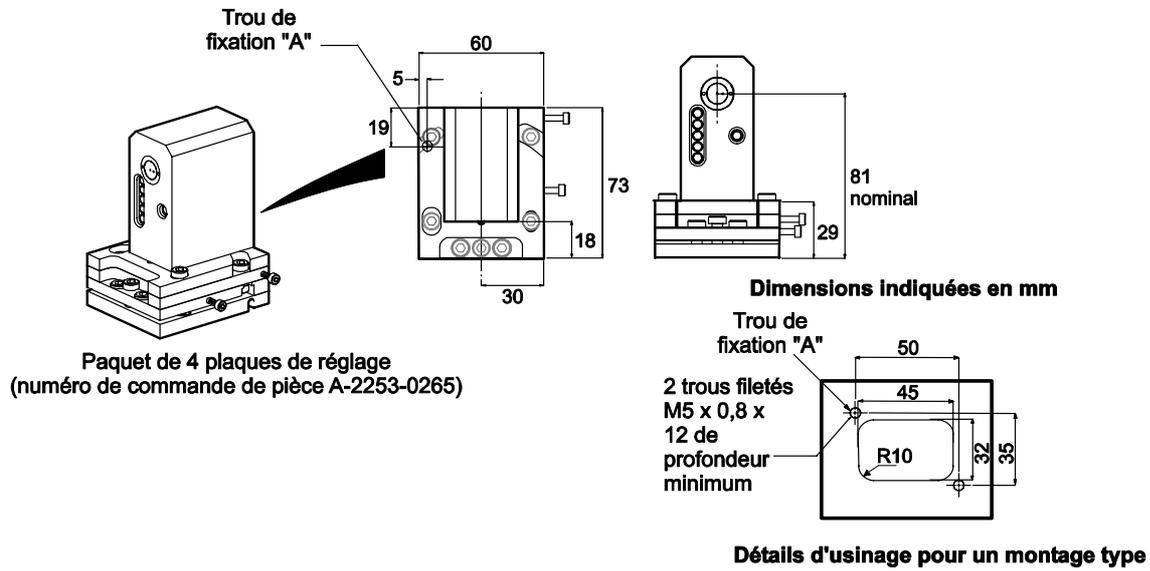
DETAILS D'USINAGE POUR MONTAGE TYPIQUE
